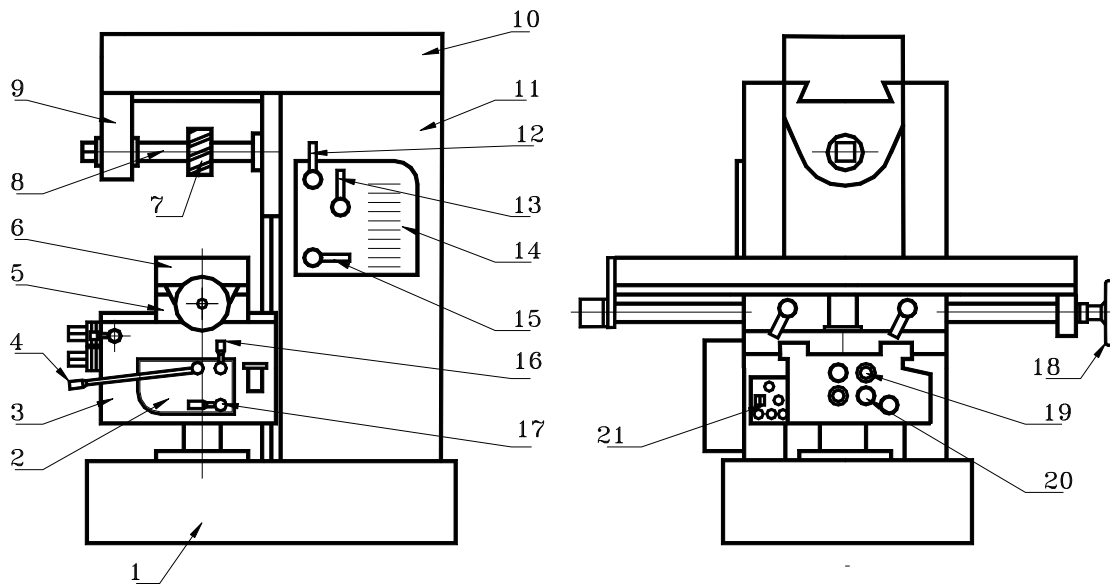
Partes principais duma fresadora universal de modelo Milko-35R.
